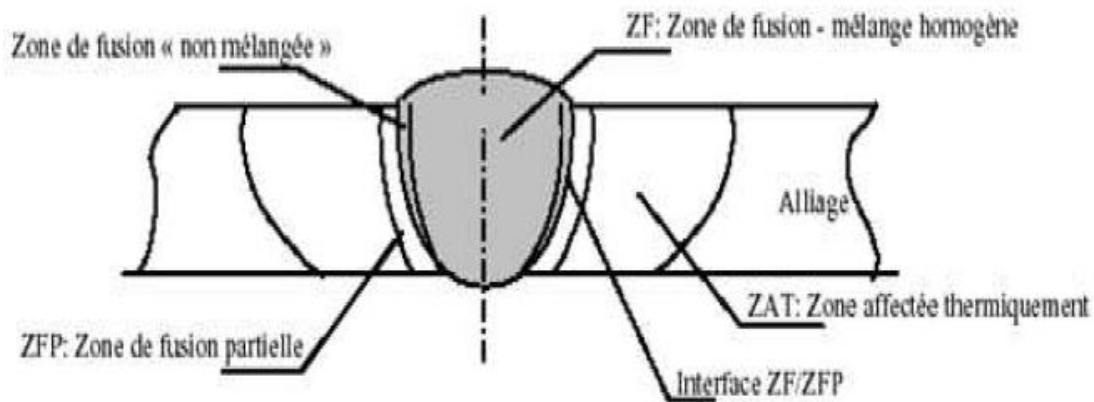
Différentes zones constituant un joint de soudure [14]
